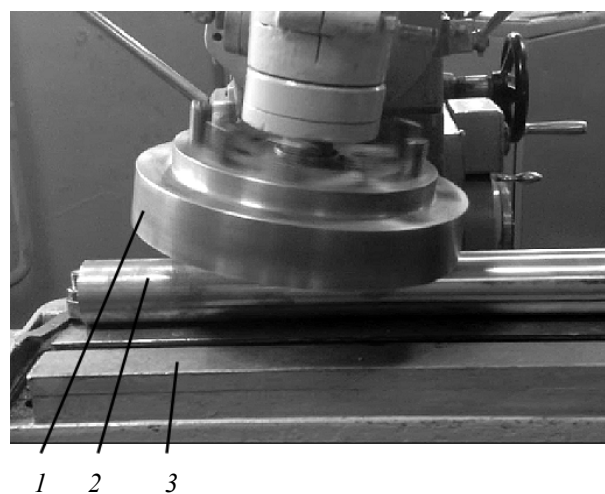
Антифрикционная обработка направляющей на вертикально-фрезерном станке:
